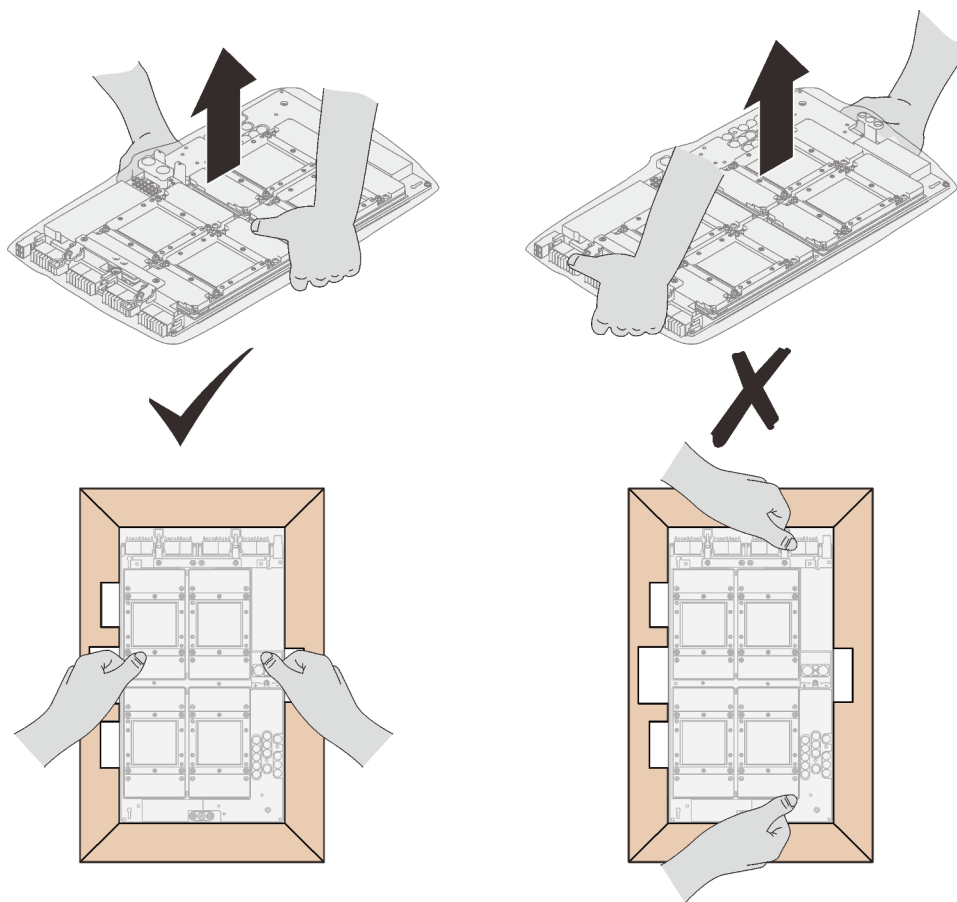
Extracción de la Placa de GPU SXM de la caja del paquete
